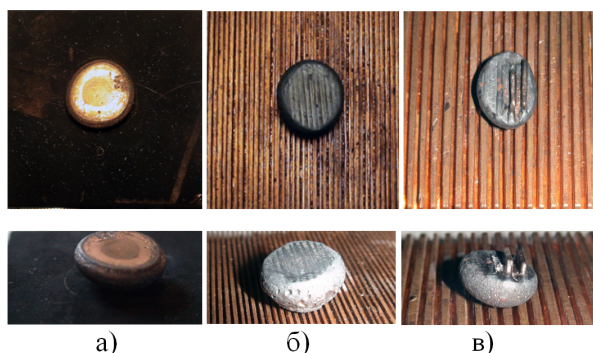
Состояние контактной поверхности капель меди, затвердевших на гладкой медной пластине (а), шероховатой с узкими (б) и широкими (в) пазами
